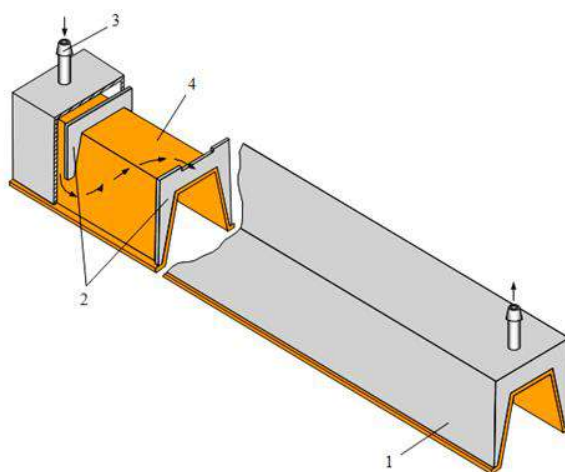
Конструкция формирующего устройства для восстановления поломанных зубьев крупномодульных шестерен: 1 – корпус; 2 – диафрагмы; 3 – входной штуцер подачи охлаждающей воды; 4 – медный формирующий кокиль.
